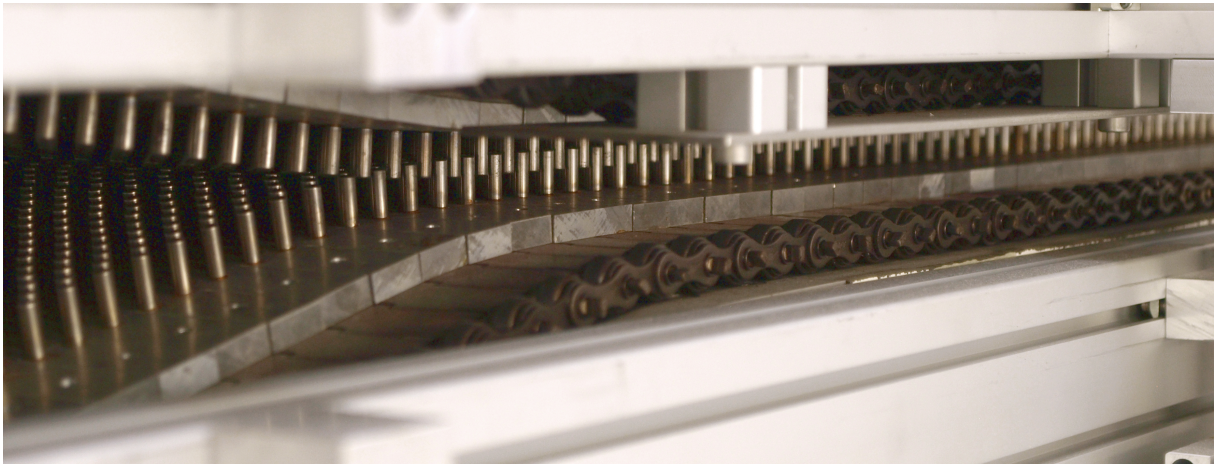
Scharnierplattenband mit aufgeschraubten Werkzeugelementen
